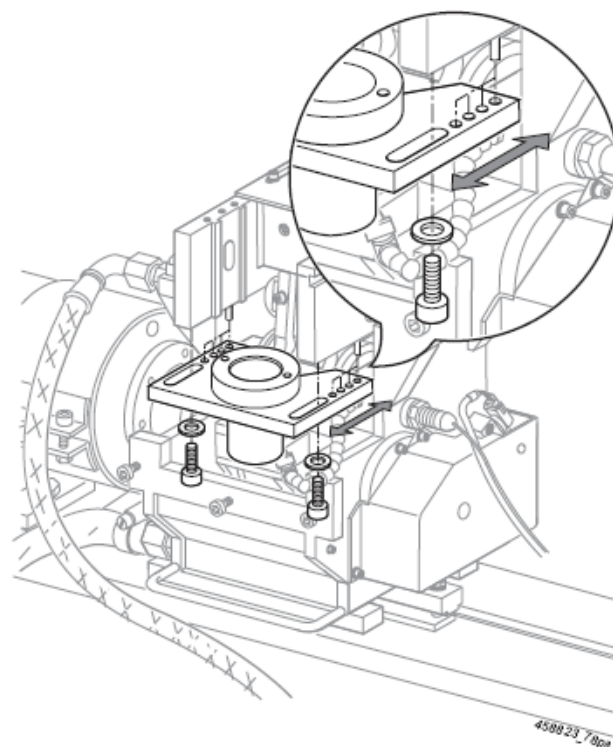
Направляющая пластина с решёткой с отверстиями.
